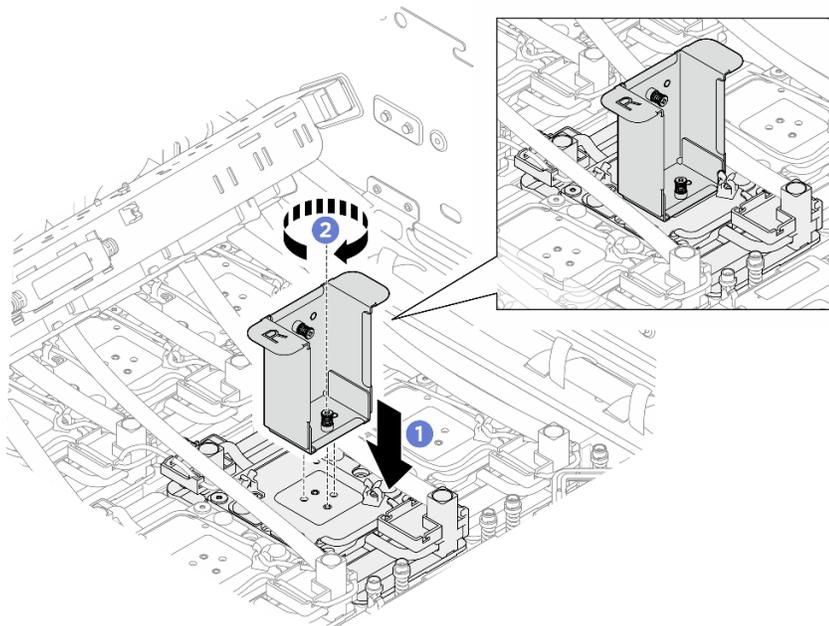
Instalando o suporte de serviço na placa fria da GPU
